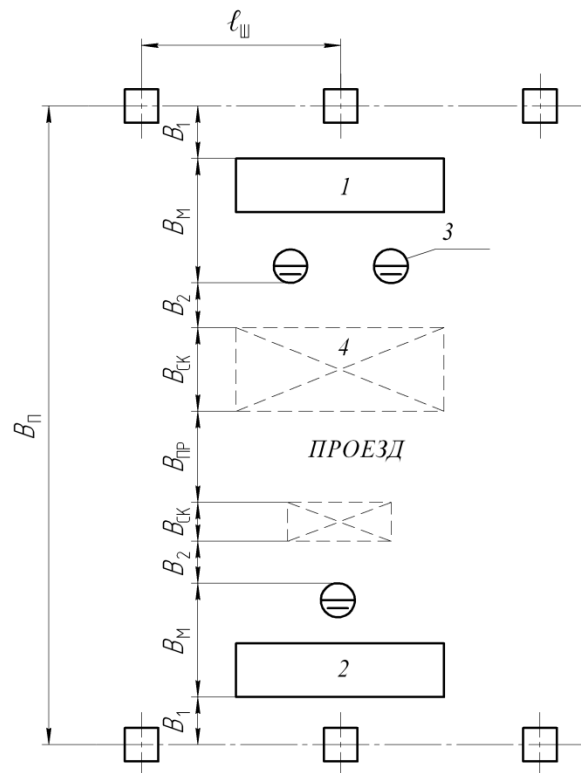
Схема планировки цеха при расположении складочных мест вдоль ряда (проезда): 1 – стенд для испытаний; 2 – сборочно-сварочный кантователь; 3 – место обслуживающего персонала; 4 – складочное место
